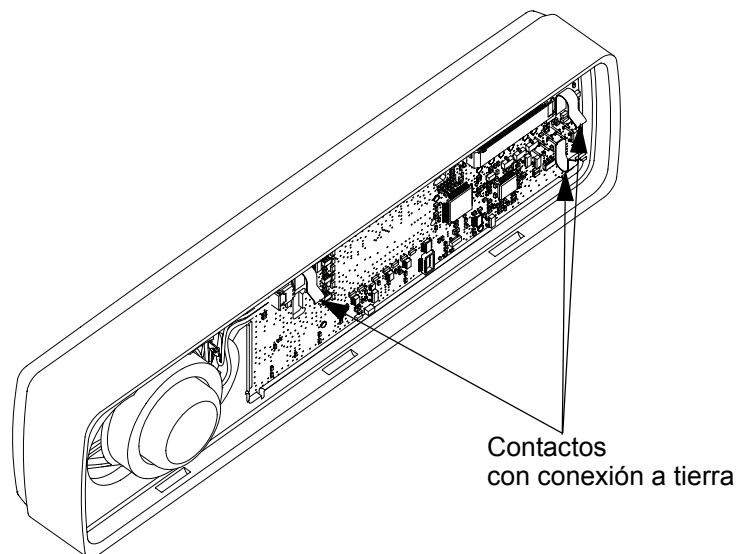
Montaje del teclado en la carcasa del cabezal
